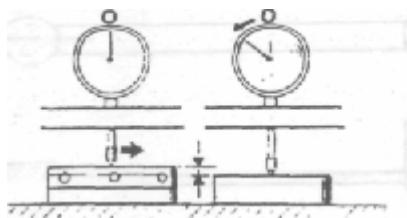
Сравнение положения установочного кольца по отношению к подшипнику при корректировке предварительного натяга подшипника дифференциала
